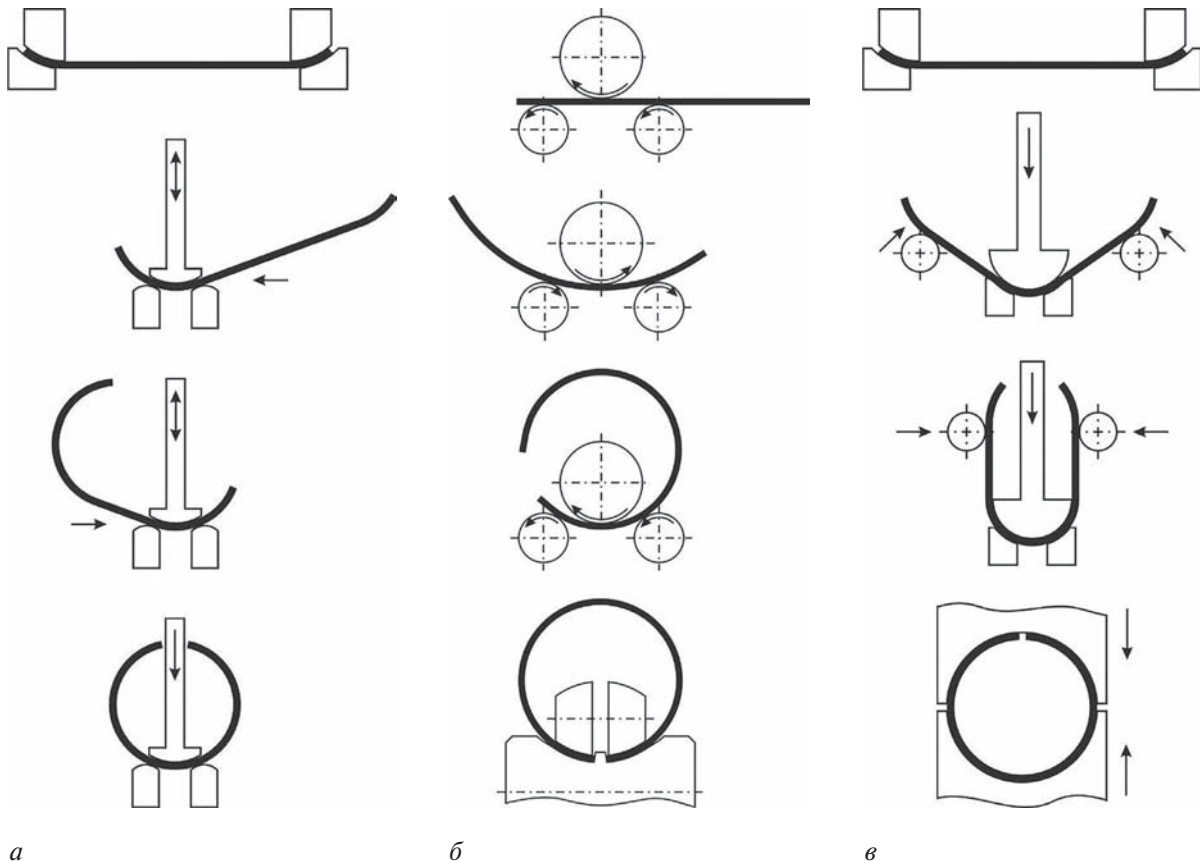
Способы формовки трубной заготовки при изготовлении прямошовных труб большого диаметра: а — шаговая формовка (JCO); б — формовка на вальцах (TBR); в — формовка на прессах (UOE)
